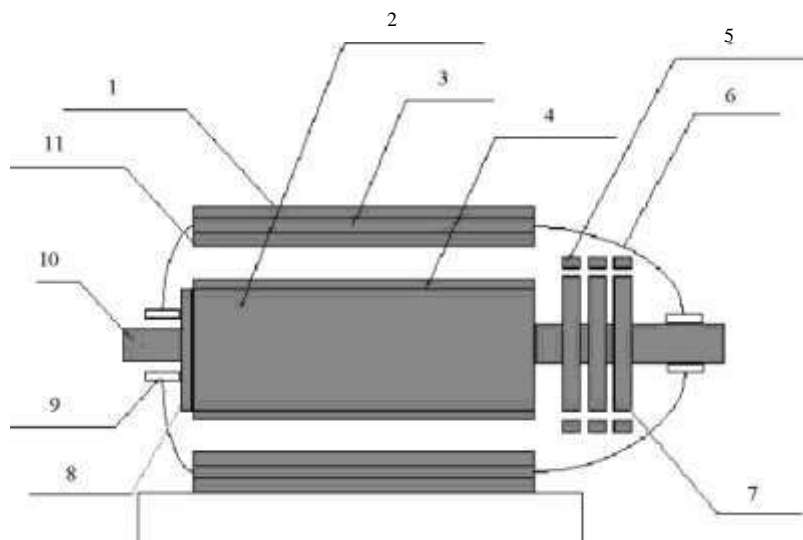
Конструкция асинхронного двигателя: 1-станина; 2-сердечник ротора; 3 — сердечник статора; 4 — обмотка ротора; 5 — щеточный аппарат; 6 — подшипниковые щиты; 7 — контактные кольца; 8 — крыльчатка вентилятора; 9 — подшипники; 10 — вал; 11 — обмотка статора
